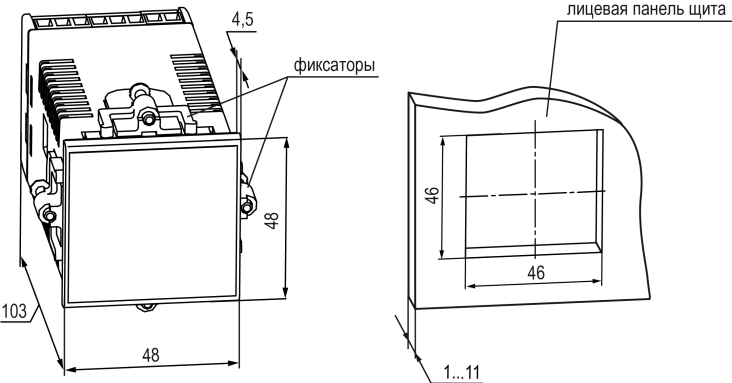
Габаритные размеры корпуса Щ5 и монтажного отверстия в щите
